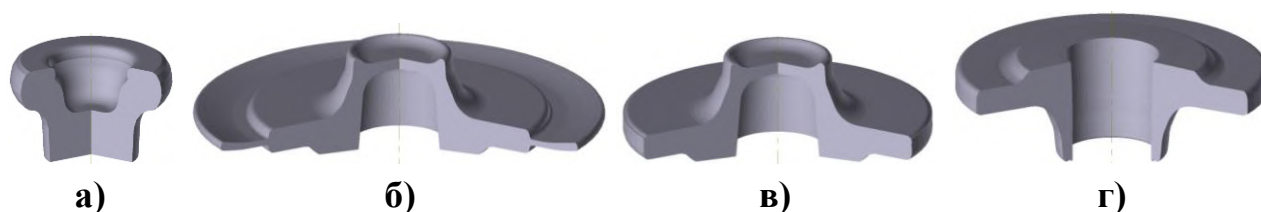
Переходы штамповки: а - предварительная штамповка, осадка, б - окончательная штамповка, в - обрезка облоя, г - пробивка отверстия
